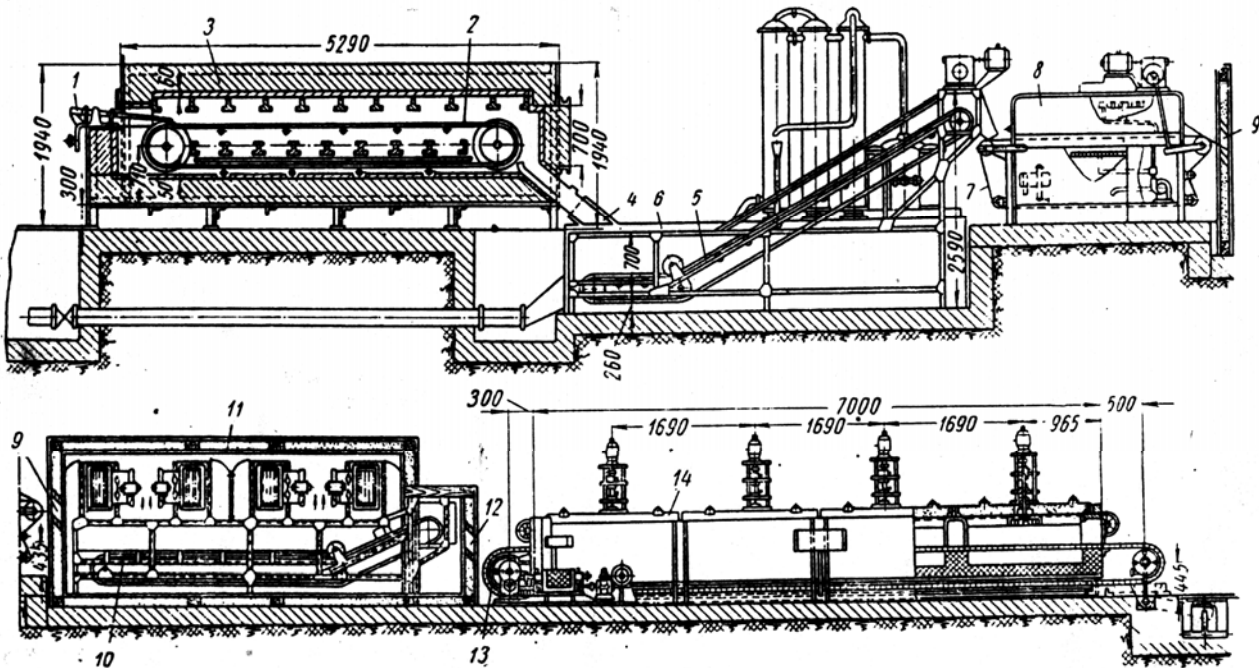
Схема потокового конвеєрного агрегата для термічної обробки кілець підшипників
